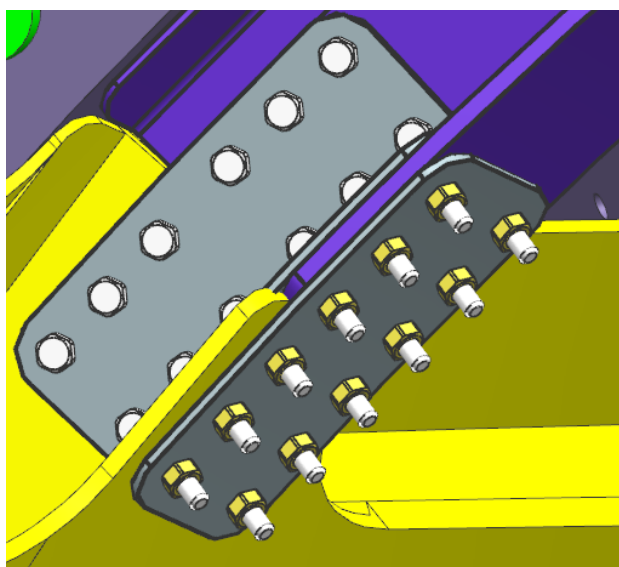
Перестыковка дуги шпангоута №5 с рамой фонаря.
